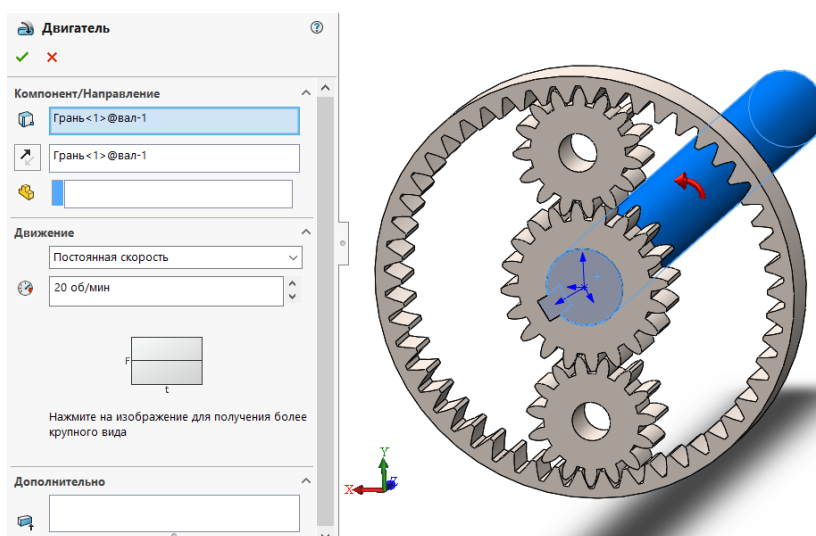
Назначение двигателя на ведущий вал планетарного механизма
